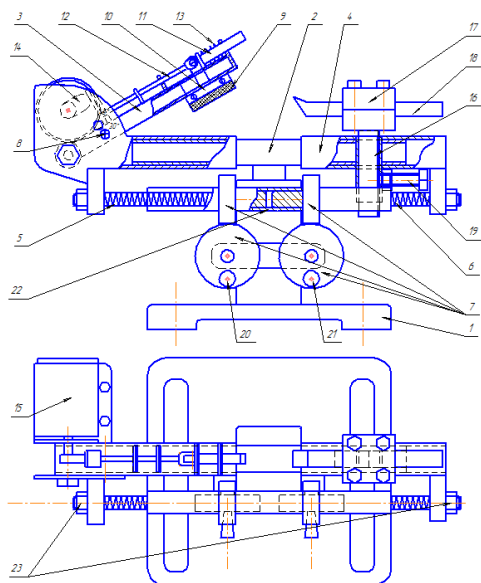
Схема приспособления для шлифования фасок и тарелок клапанов двигателей
